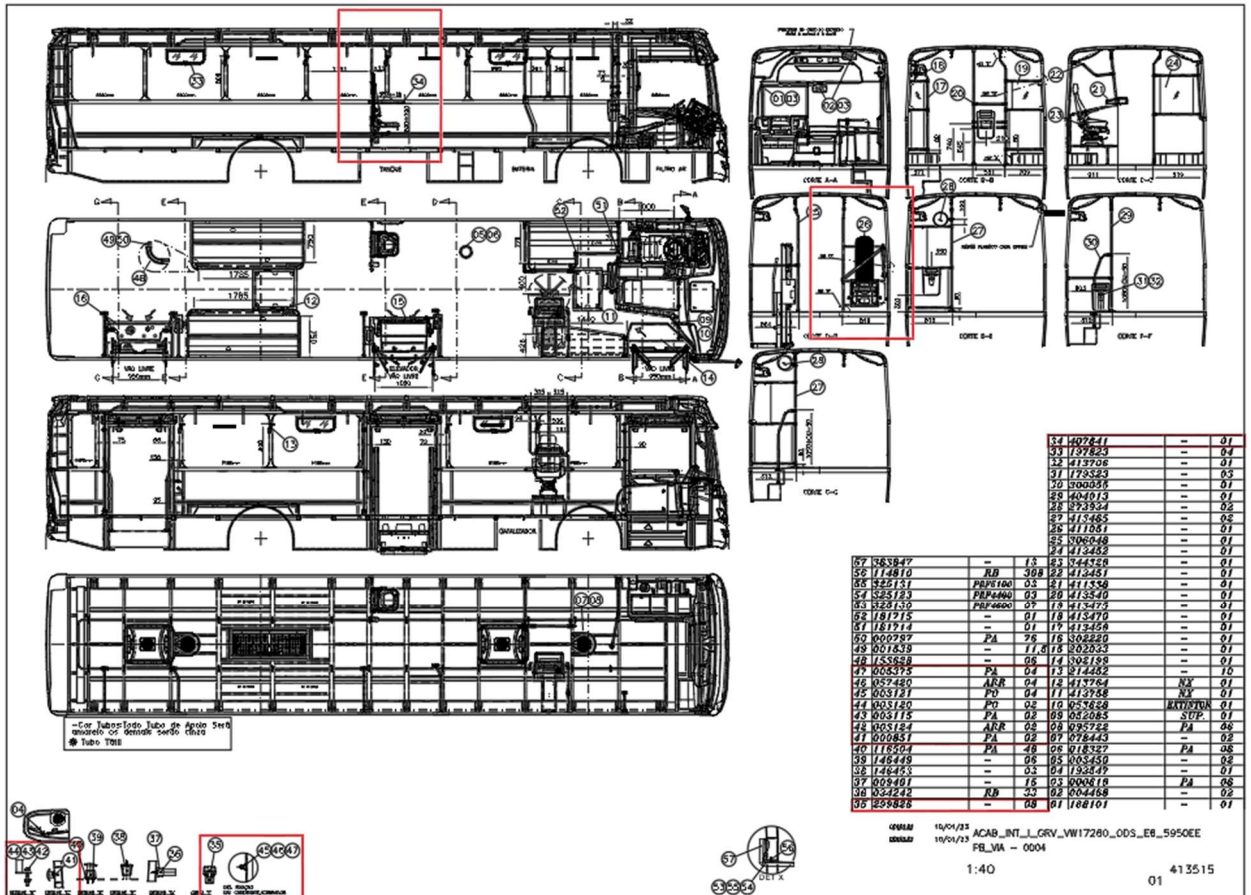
Projeto esquema de montagem divisória do cadeirante
